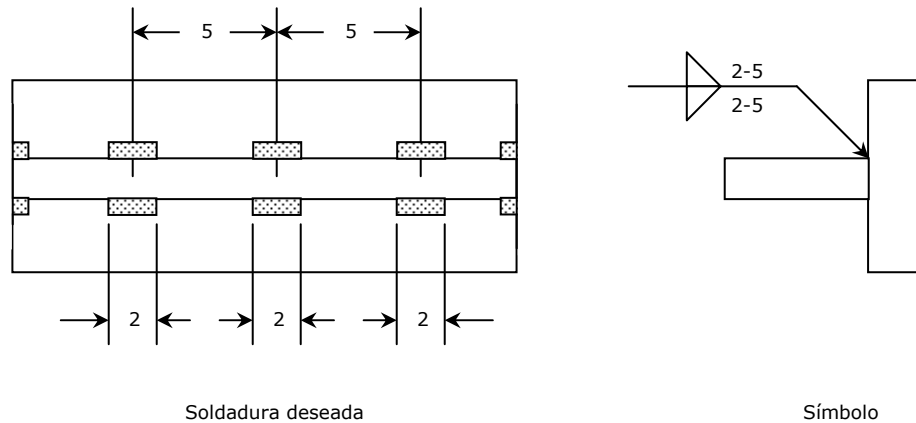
Símbolo de soldadura que aplica para ambos lados de la unión
